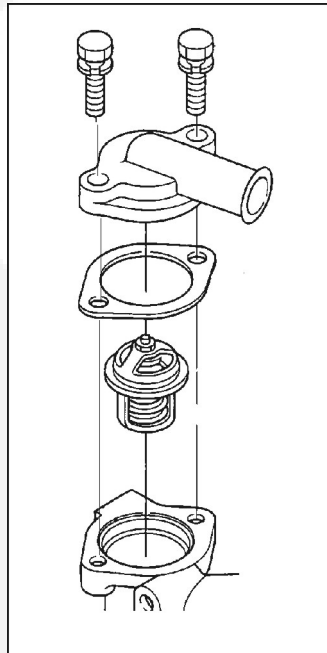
THERMOSTAT ET BOÎTIER TYPES
